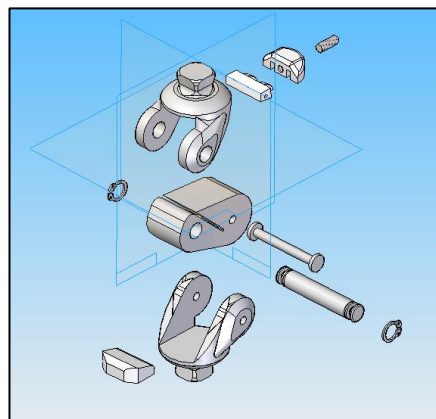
Vista explosionada del encaje con el conector de la rodilla. Solid Edge.
